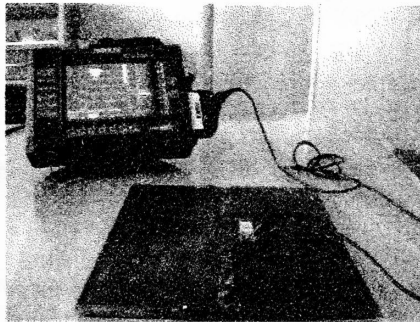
Загальний вигляд досліджуваного зварного з'єднання
